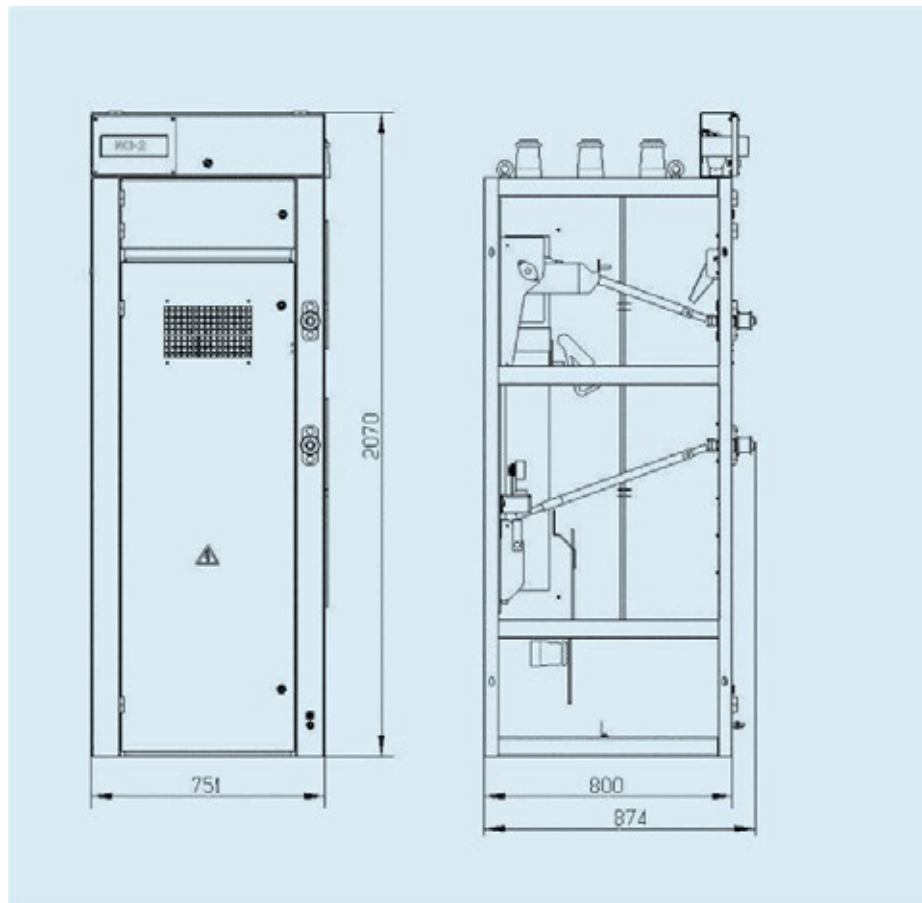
Общий вид и габаритные размеры камеры КСО-305
